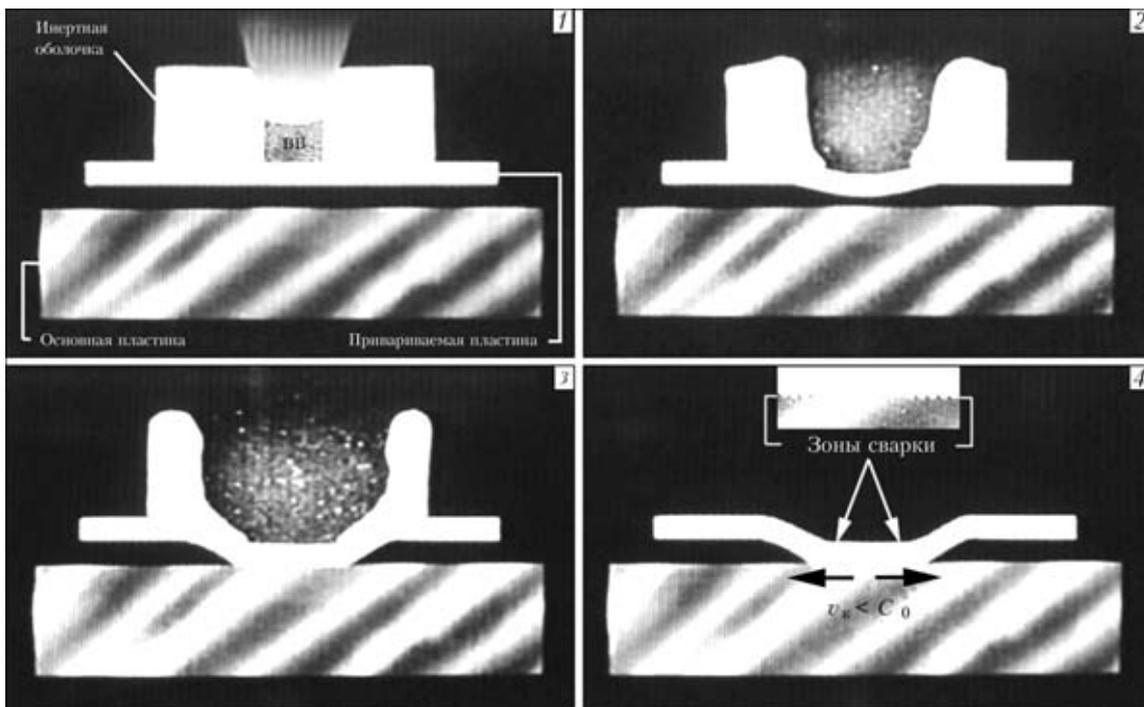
Кинематика процесса точечной (линейной) сварки цилиндрическим зарядом ВВ, помещенным в оболочку из инертного материала: 1-4 — кадры последовательности процесса
